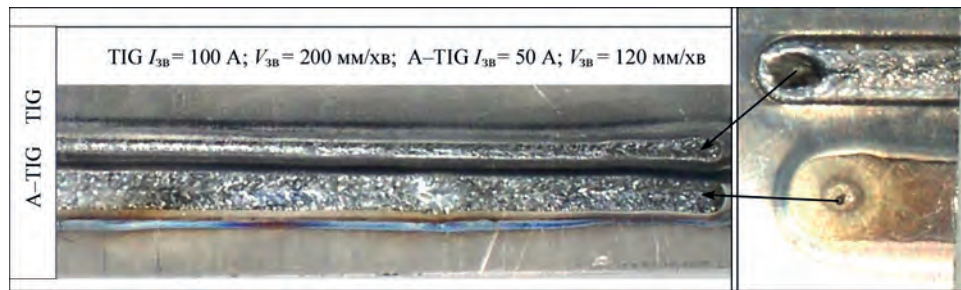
Зовнішній вигляд поверхні зварних швів при повному проплавленні, виконаних TIG та А-TIG зварюванням титанового сплаву ВТ-20 завтовшки $\delta = 2$ мм при однаковій швидкості зварювання $V_{зв} = 200$ мм/хв: зверху – А-TIG шов, струм зварювання 50 А; знизу – TIG шов, струм зварювання $I_{зв} = 100$ А (результати особистих досліджень)
